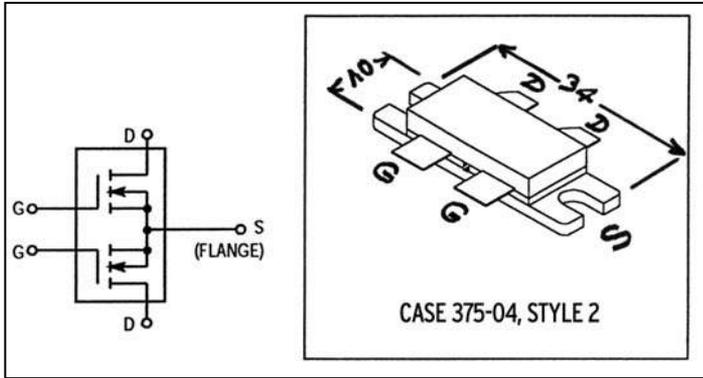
Vue du boîtier et schéma interne du transistor Motorola® MRF-151G. Dimensions approximatives en mm.
